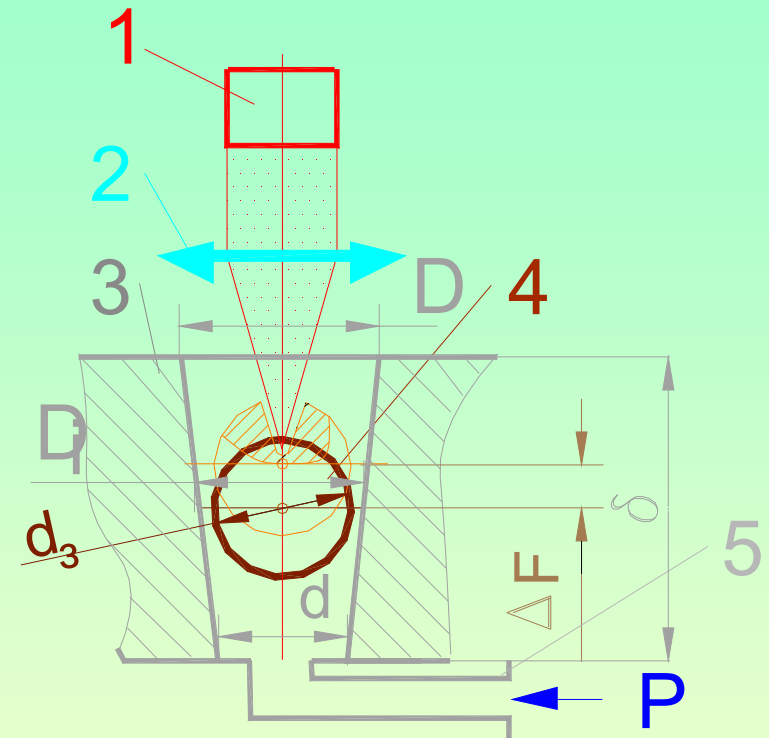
Схема обробки отворів у заготовці (рис. 3.24).
